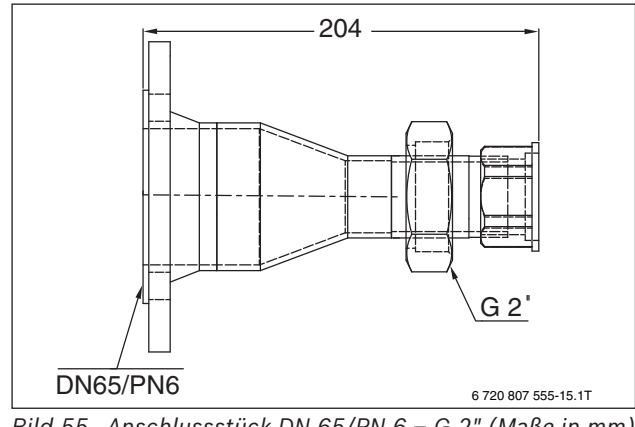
Anschlussstück DN 65/PN 6 – G 2" (Maße in mm)
